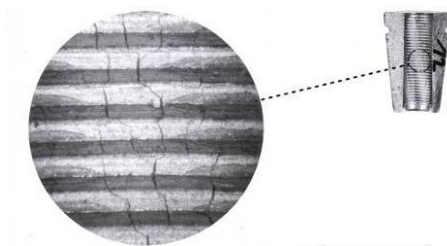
Pequenas fissuras (tamanho de um cabelo) não são sinal para alarme, mas assim que estas aumentem deve-se proceder à sua substituição
